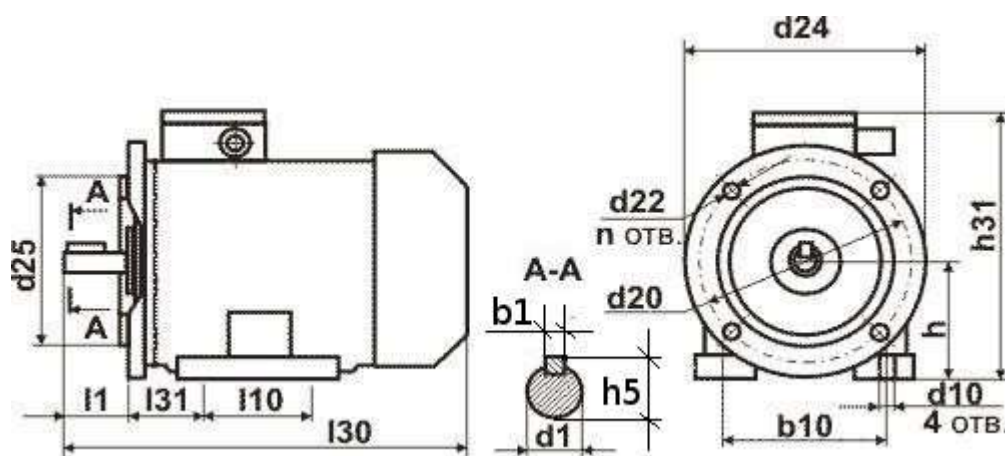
габаритно-присоединительные размеры двигателя АИР160М2.
